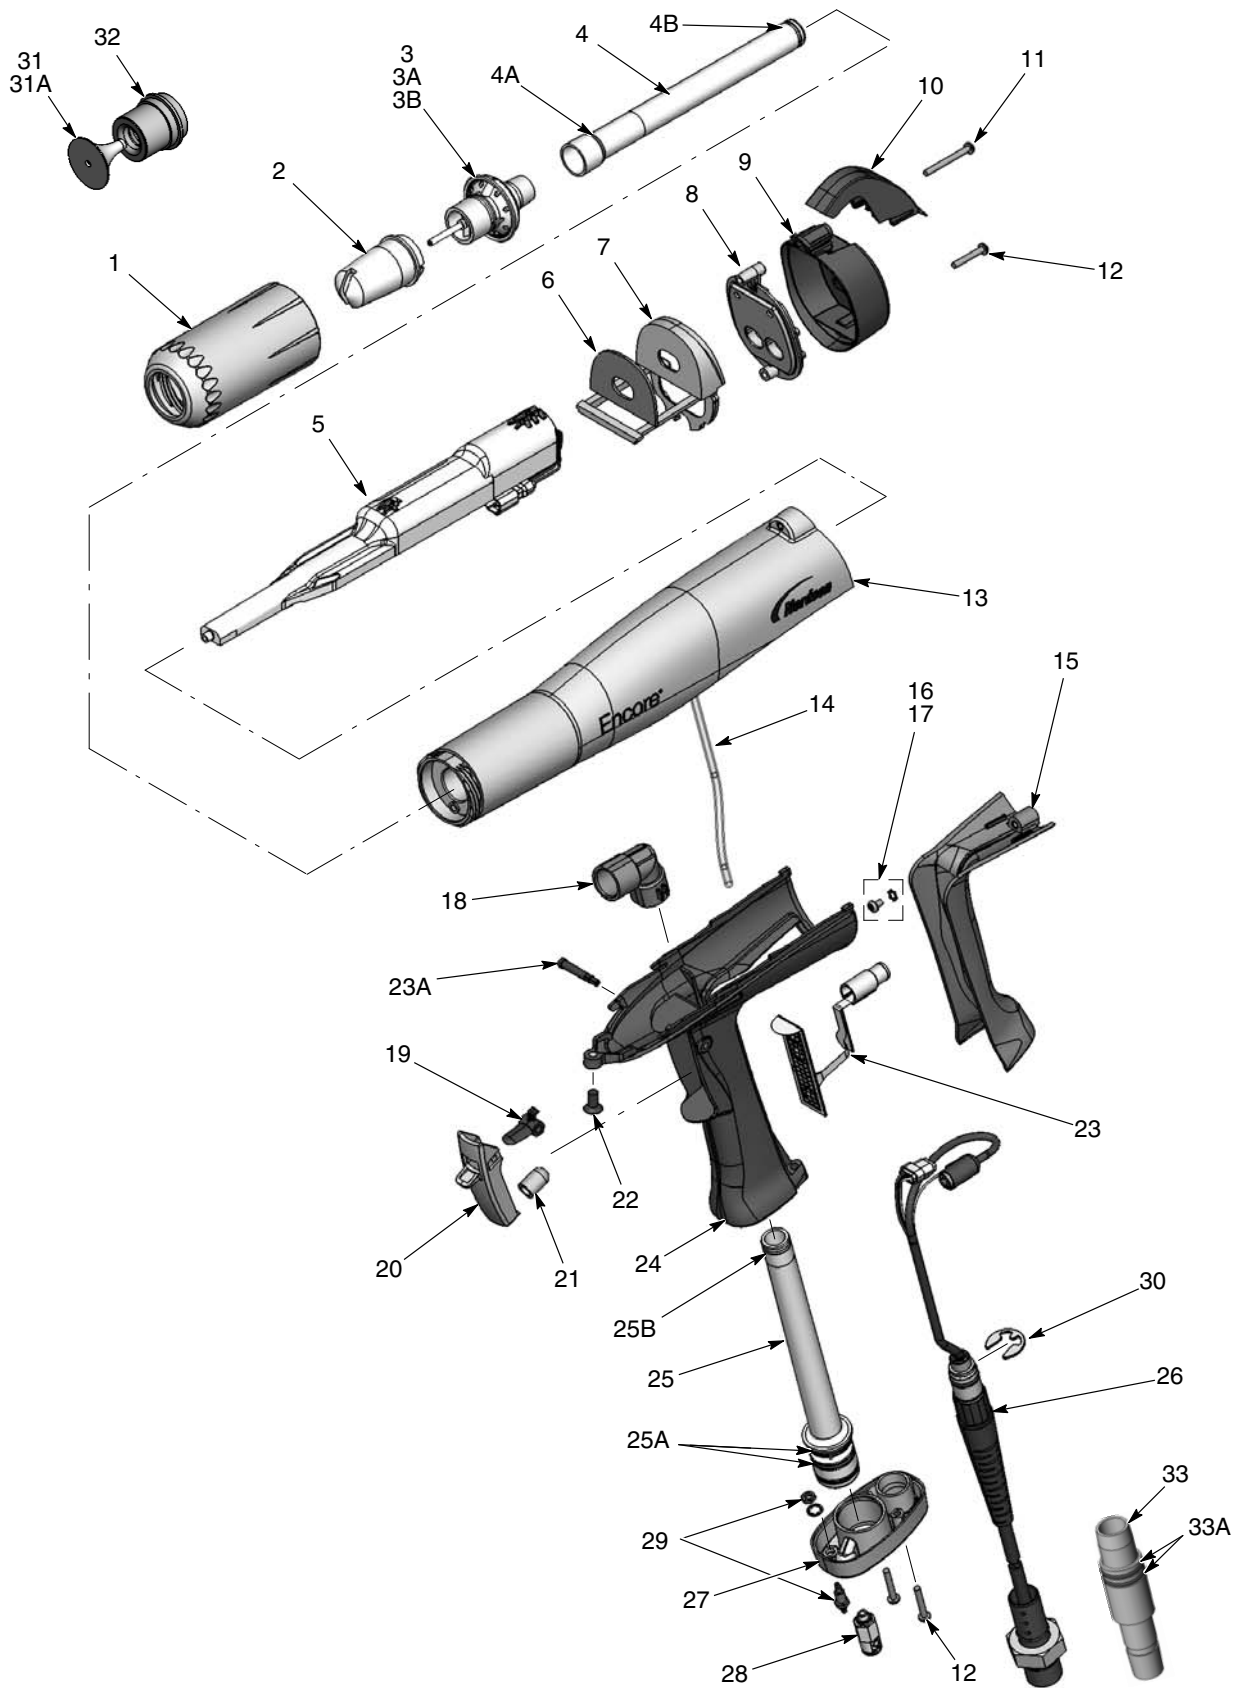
Объемный вид с разделением деталей ручного распылителя Encore и принадлежностей
